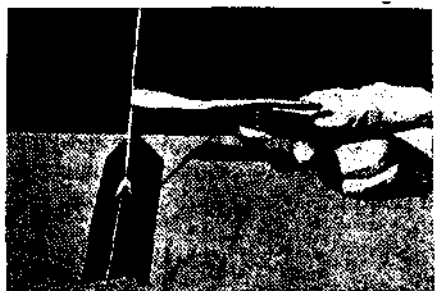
Сварка угольника по способу Бенардоса.
